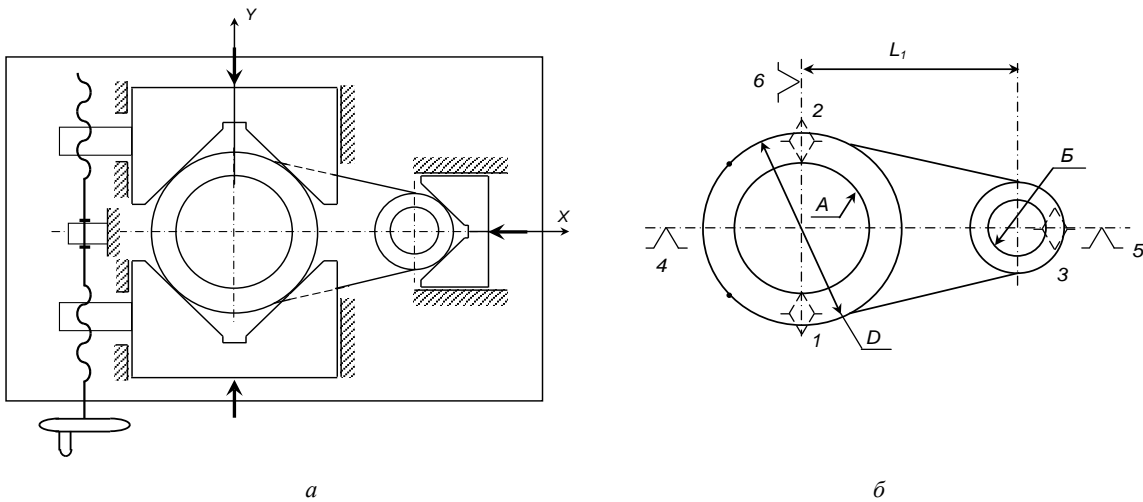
a* — конструктивна схема верстатного пристрою за варіантом 3 з установленою вихідною заготовкою;
